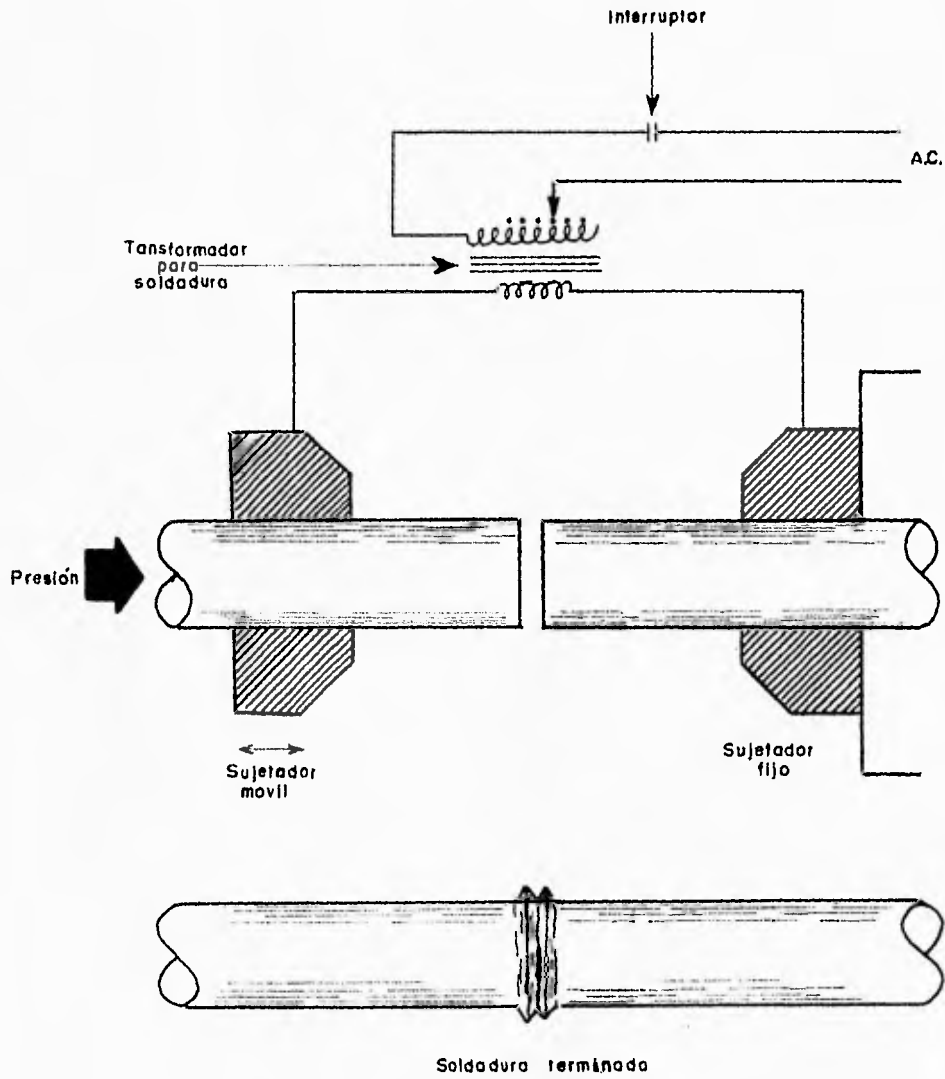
Soldadura por arco con presión (FW)
